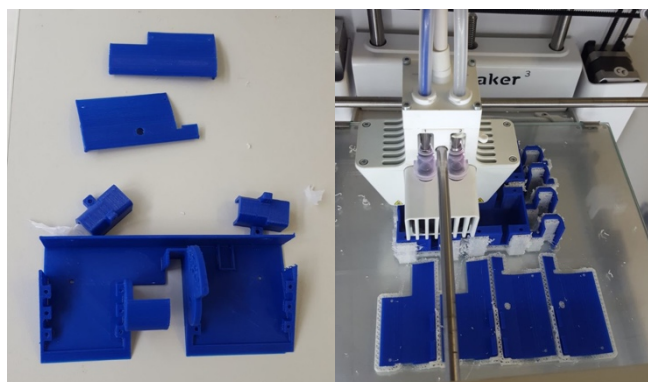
chassi, tampas e suportes de motores impressos. Fonte: autora.
